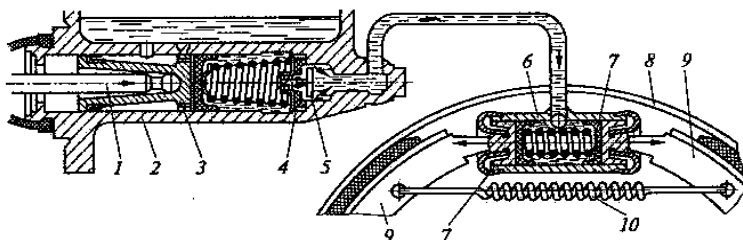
Схема тормозного механизма с гидравлическим приводом:
